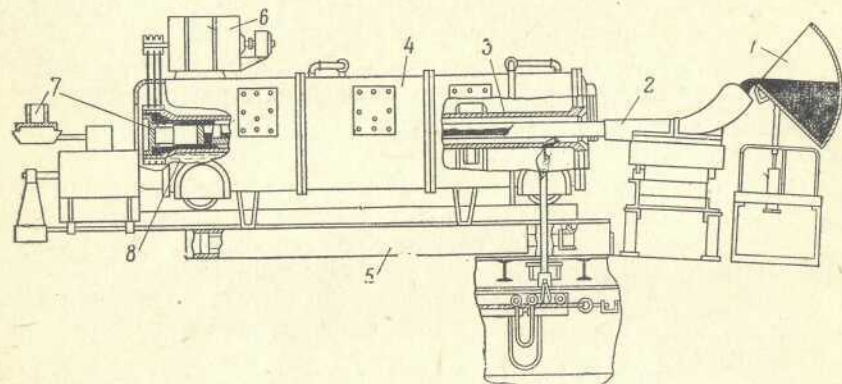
Схема центробежной машины для отливки чугунных труб
